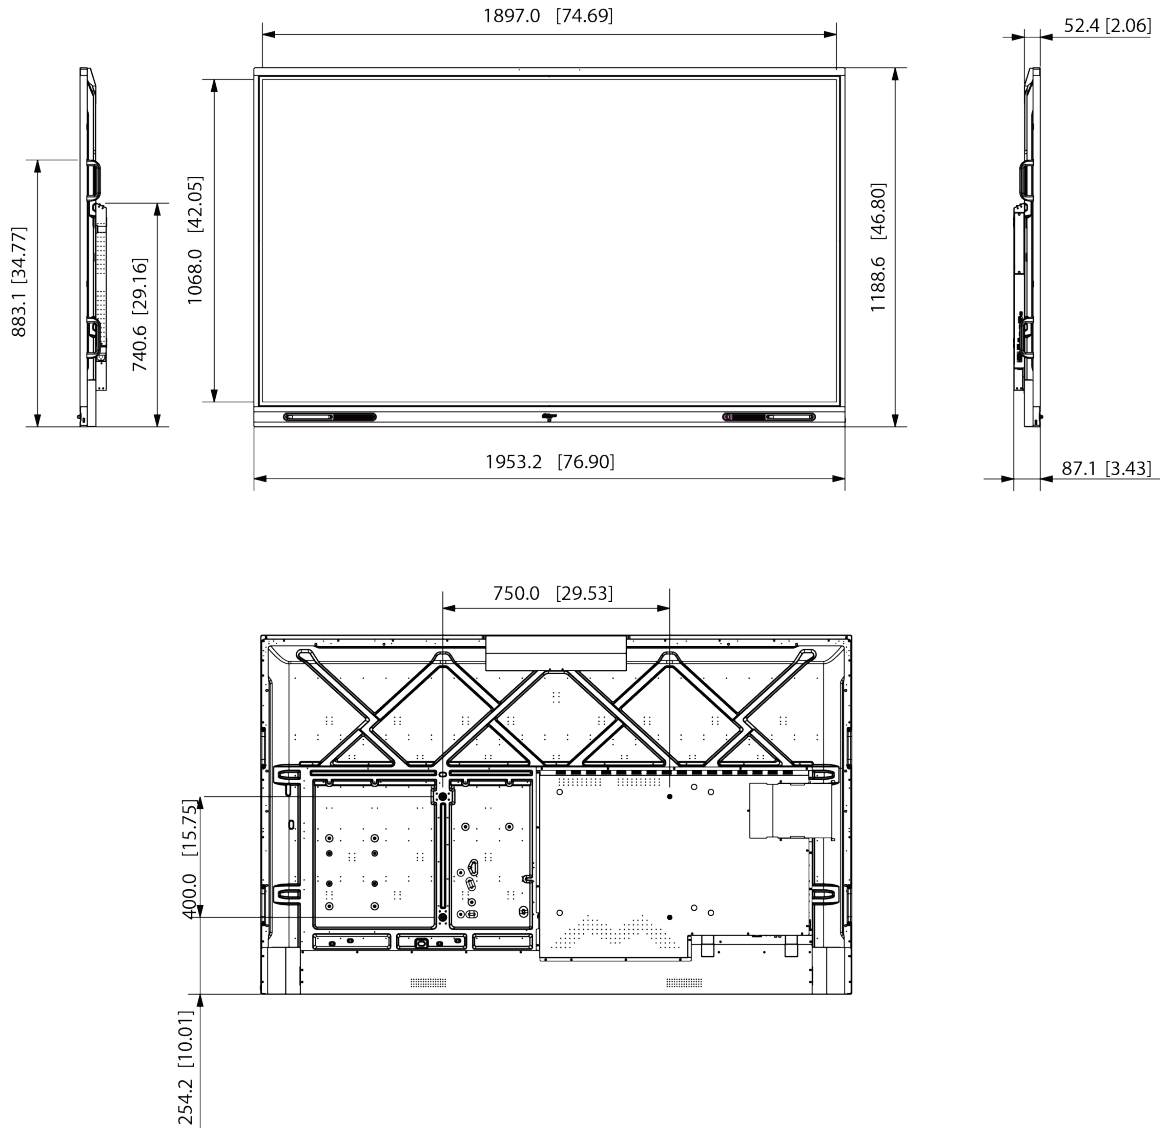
Dimensions (sans caméra) (mm [pouces])
